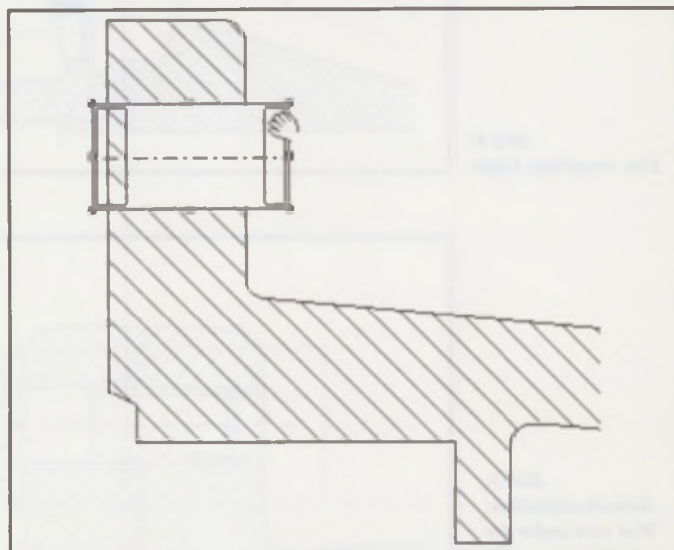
Derselbe Ausschnitt wie Bild 1 wird von CAD project gezeichnet.
